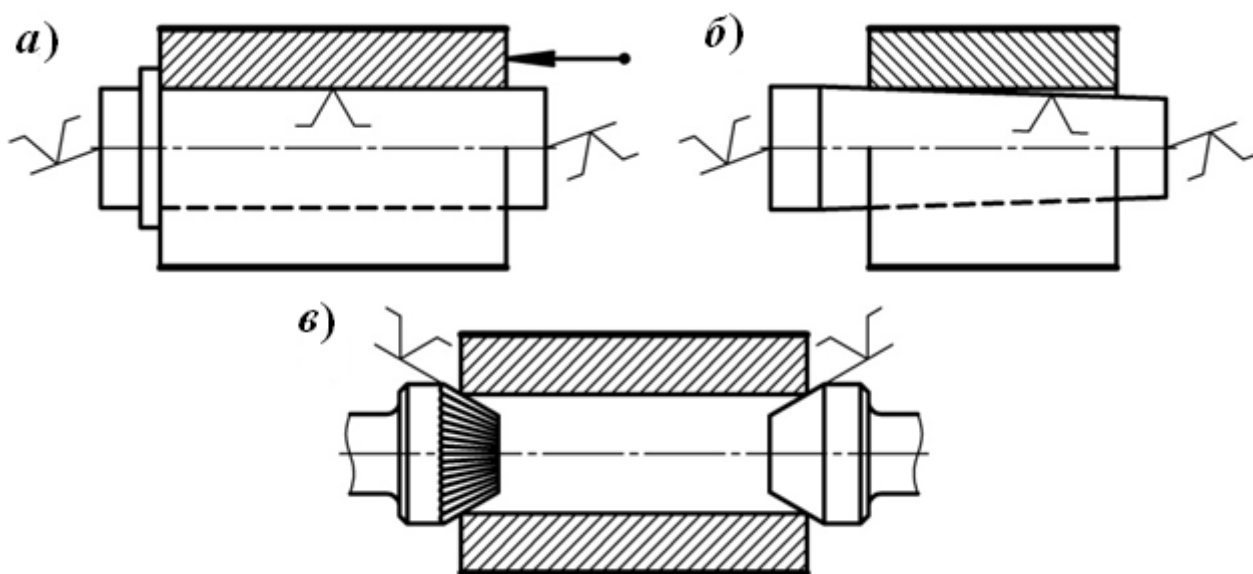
Базирование заготовок насадного инструмента на цилиндрической оправке (а), на конической оправке (б), в рифлёных центрах (в)
